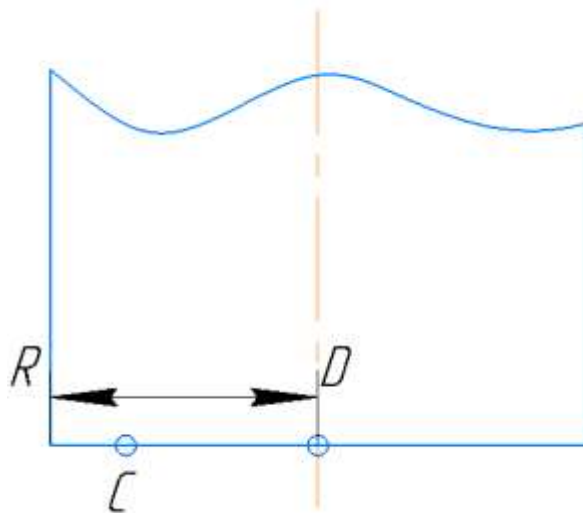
Схема визначення розрахункової висоти вершини кінцевої циліндричної фрези при зіткненні з точкою С на контрольованій поверхні: R- радіус циліндричної частини фрези, D- вершина кінцевої циліндричної фрези
